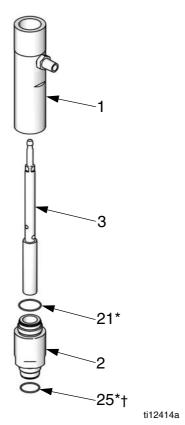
Assembler l'ensemble piston/tige aux cylindres
